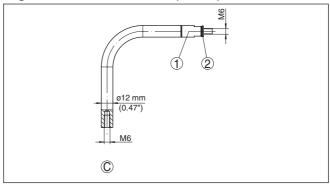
Componentes de varilla - ø 12 mm (0.47 in) - Segmento de arco
